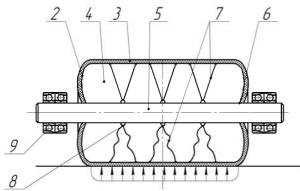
Колесо с широкопрофильной шиной низкого или сверхнизкого давления
